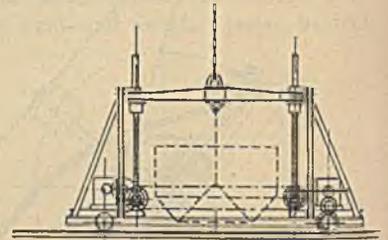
Motorwagen für Aushilfsbetrieb.
